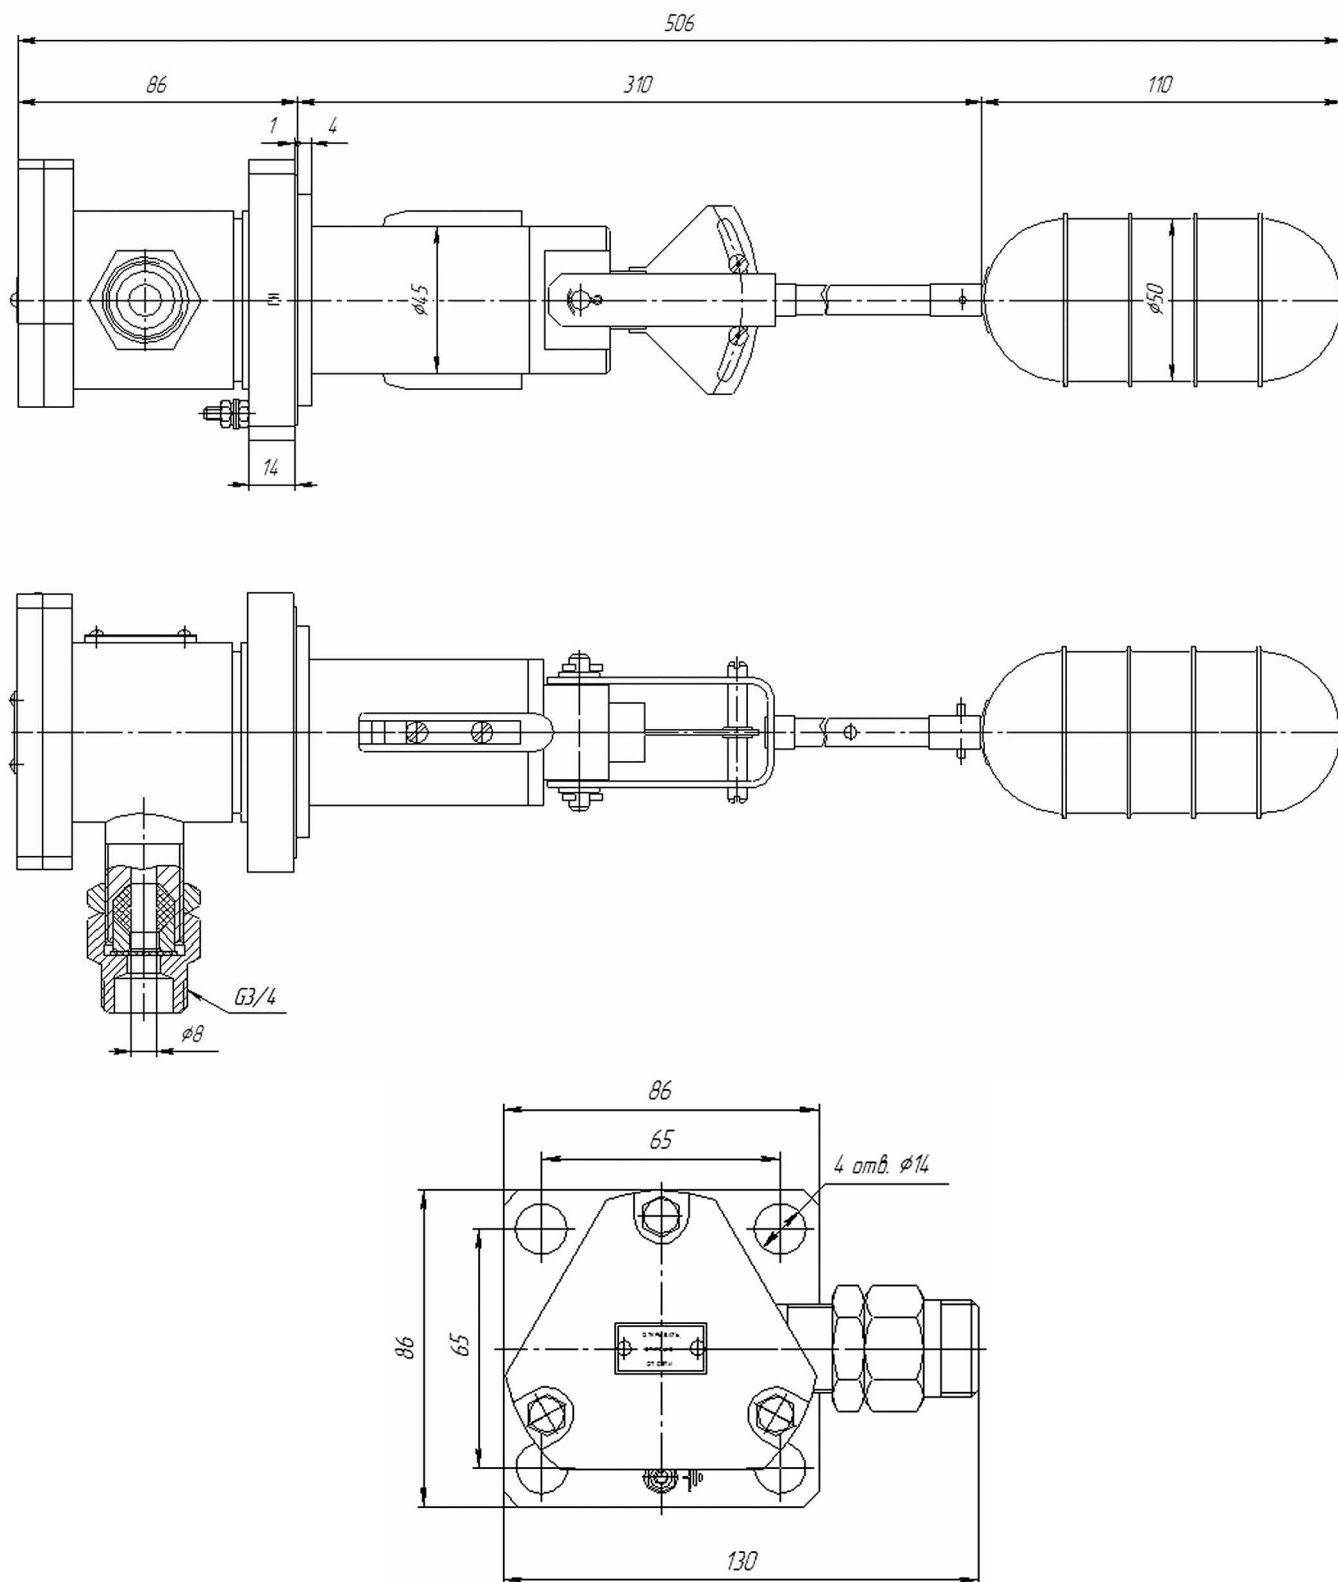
Габаритные и присоединительные размеры реле РУ-305С
